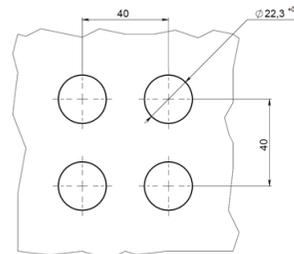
Размеры установочных отверстий для цилиндрических выключателей
